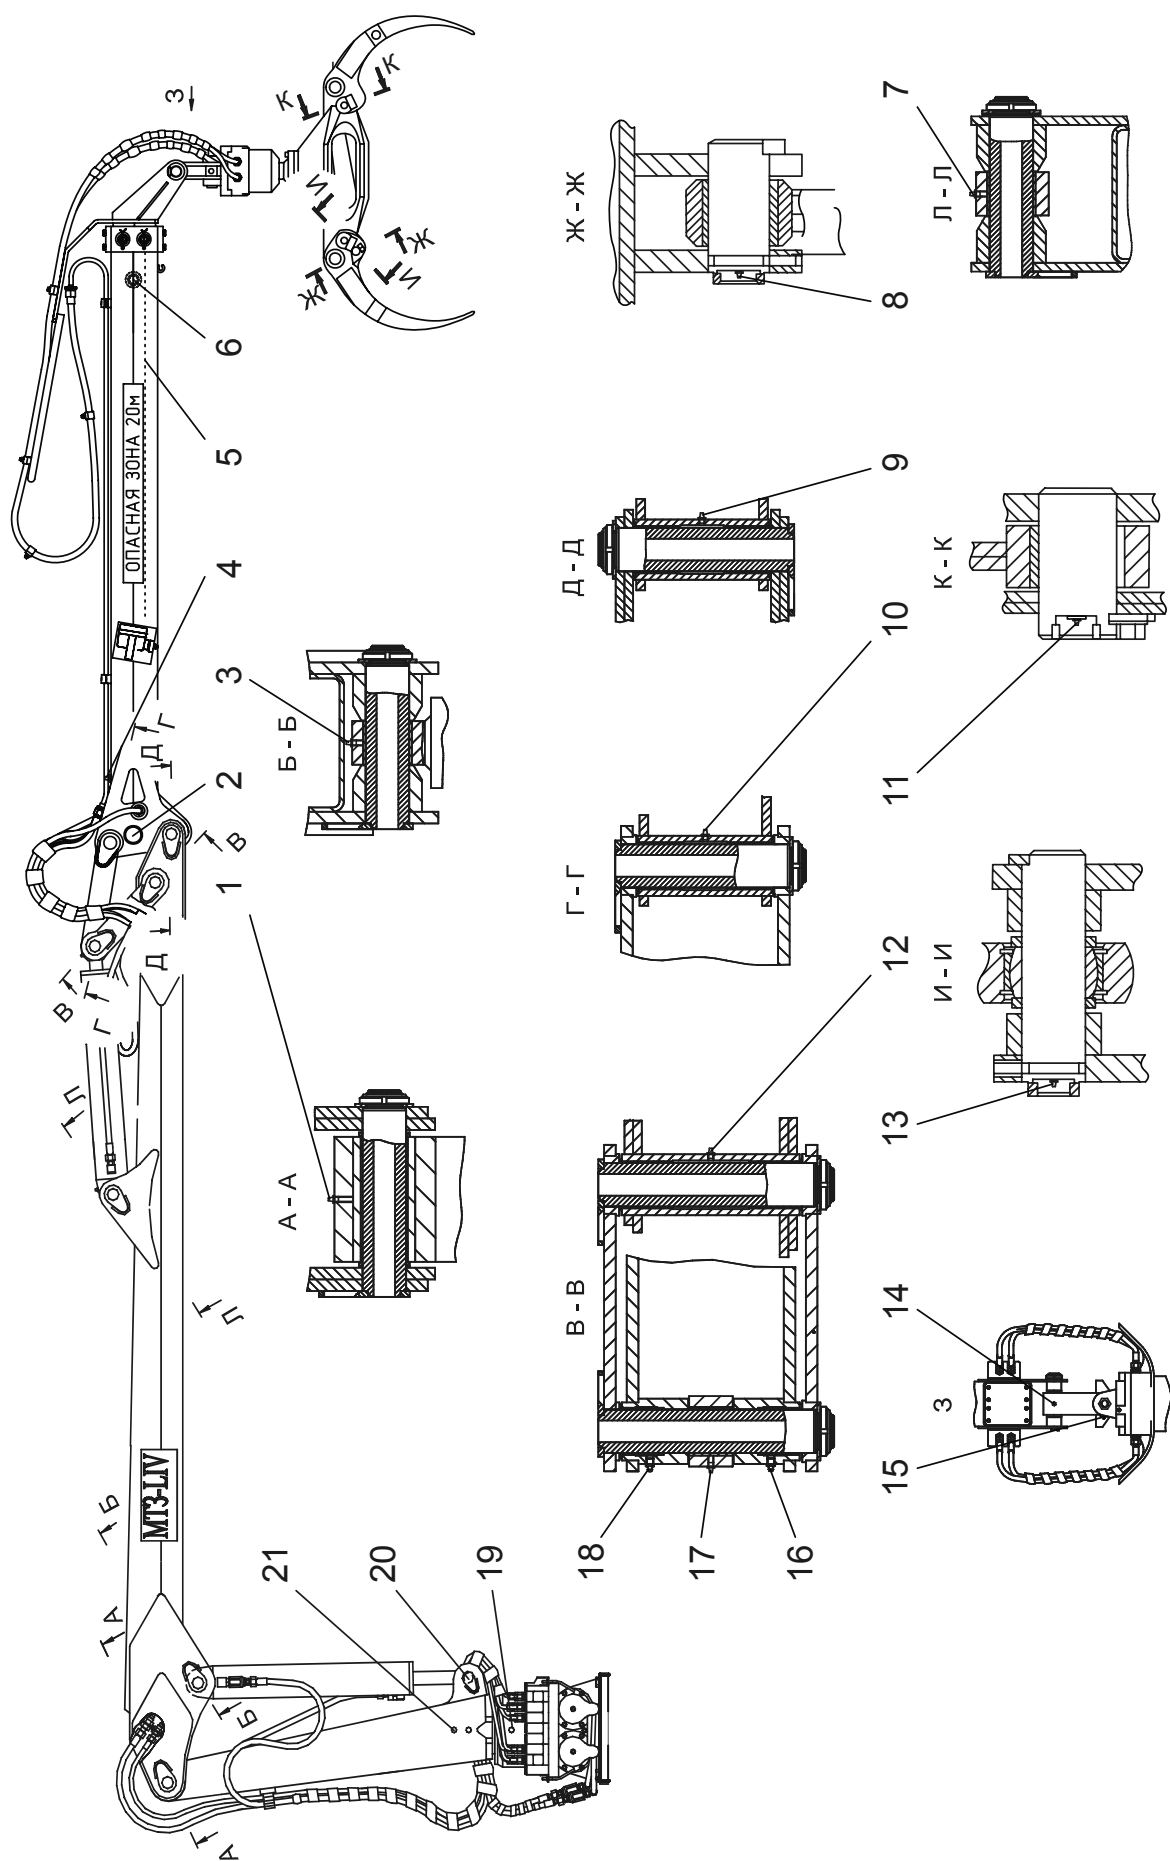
Схема смазки (заправки) манипулятора ГМ-50-01
